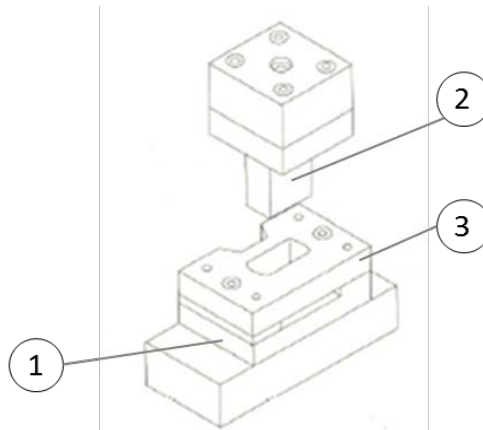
Exemplo ferramenta guiada por placa de guia ou extrator fixo 1 – Matriz ; 2 – Punção; 3 – Extrator [10]
